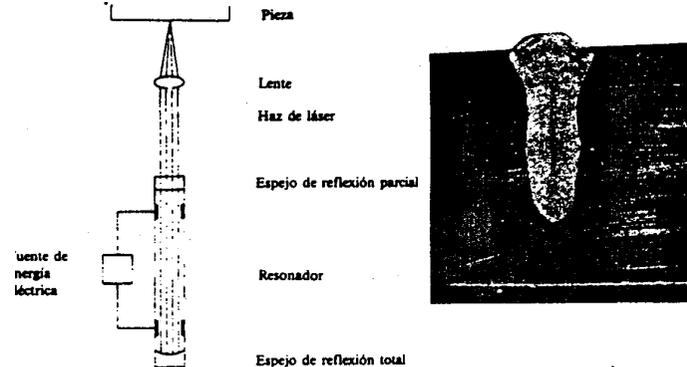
Soldadura por láser: a) Esquema representativo.
